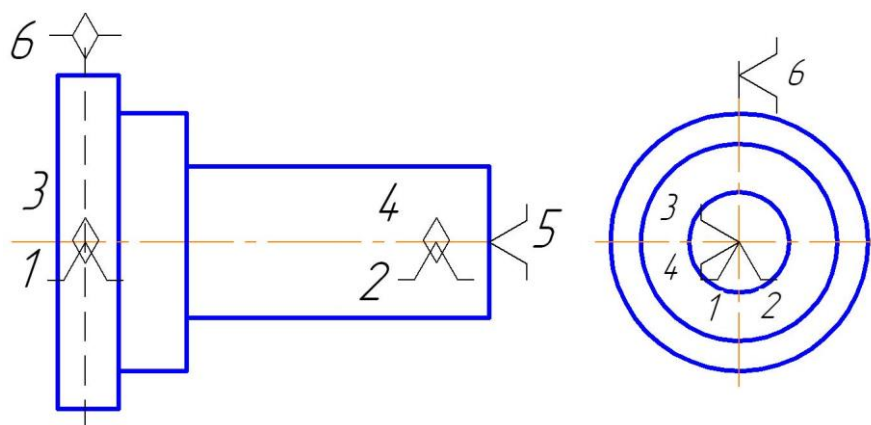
Теоретична схема базування на свердлувальному верстаті з ЧПК
